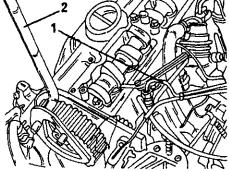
Проверка зазоров клапанов с помощью щупа (1). Распределительный вал можно проворачивать специальным приспособлением.
